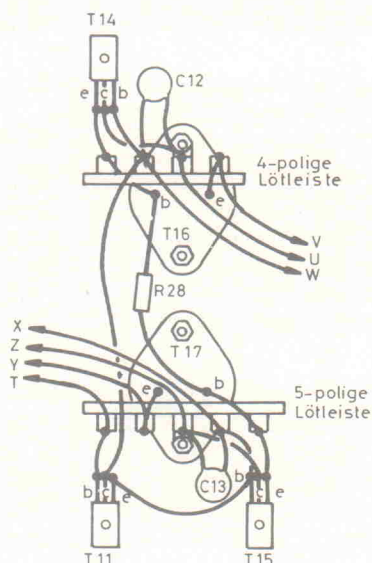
Verdrahtung der Bauelemente auf dem Kühlkörper.
